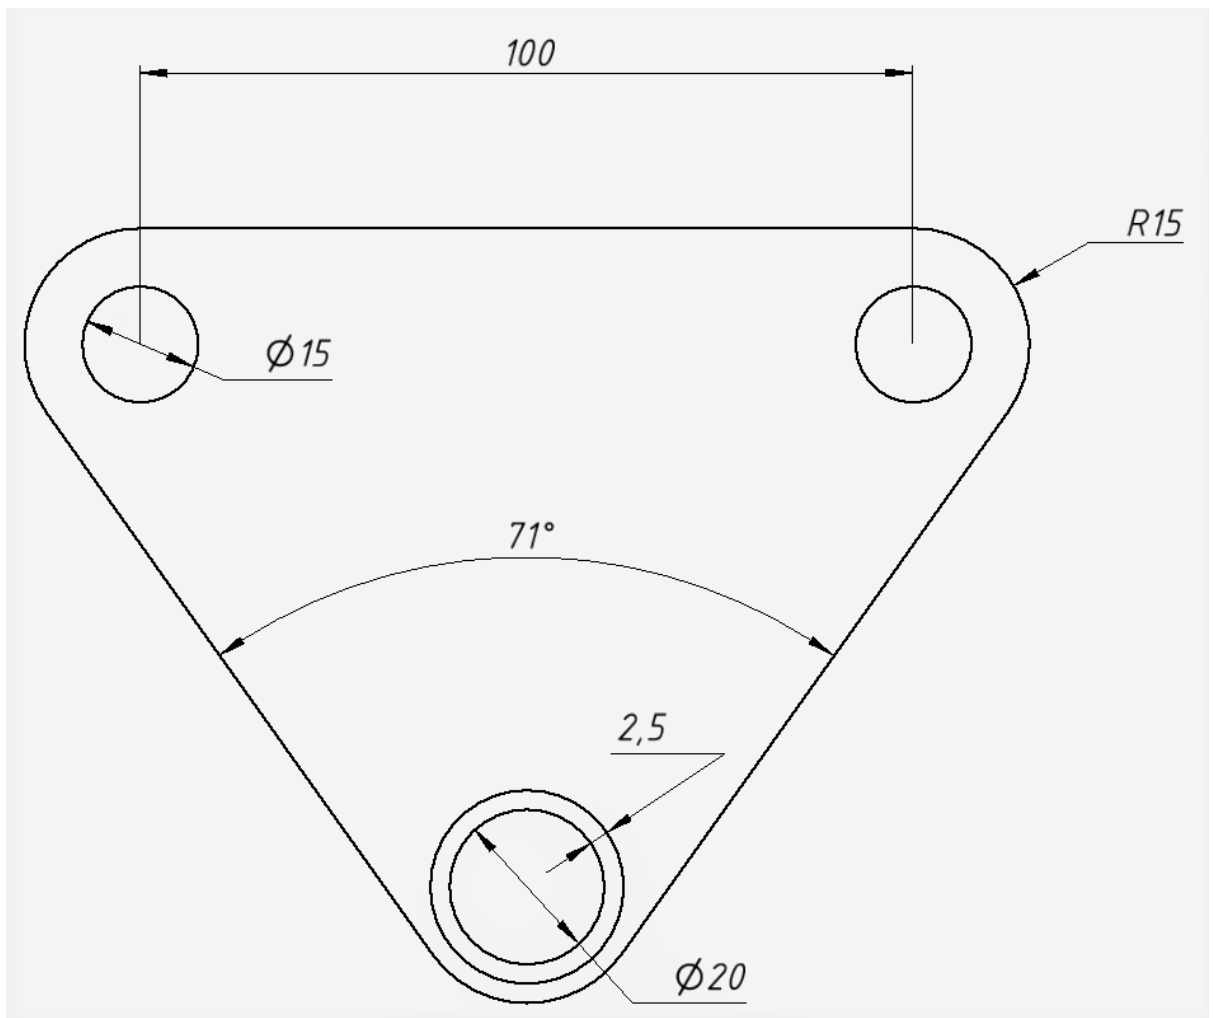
Габаритні розміри трикутного рульового механізму
